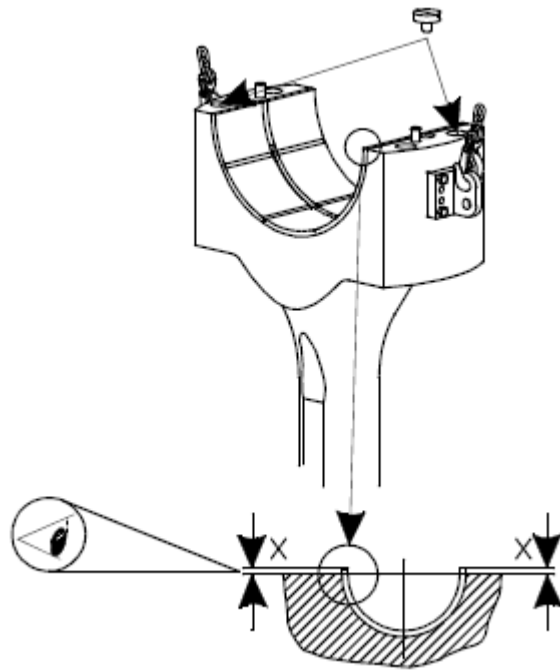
Установка нижнього вкладиша крейцкопфного підшипника
